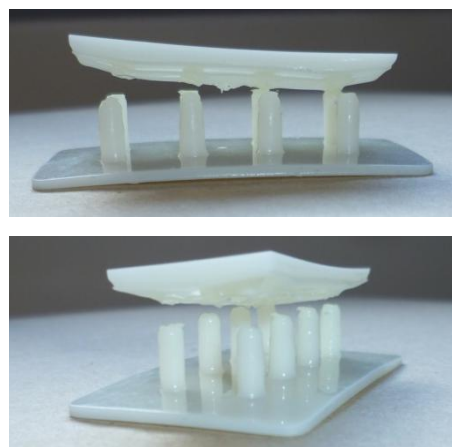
Pieza probeta 3. Arriba, vista frontal. Abajo, vista isométrica.
